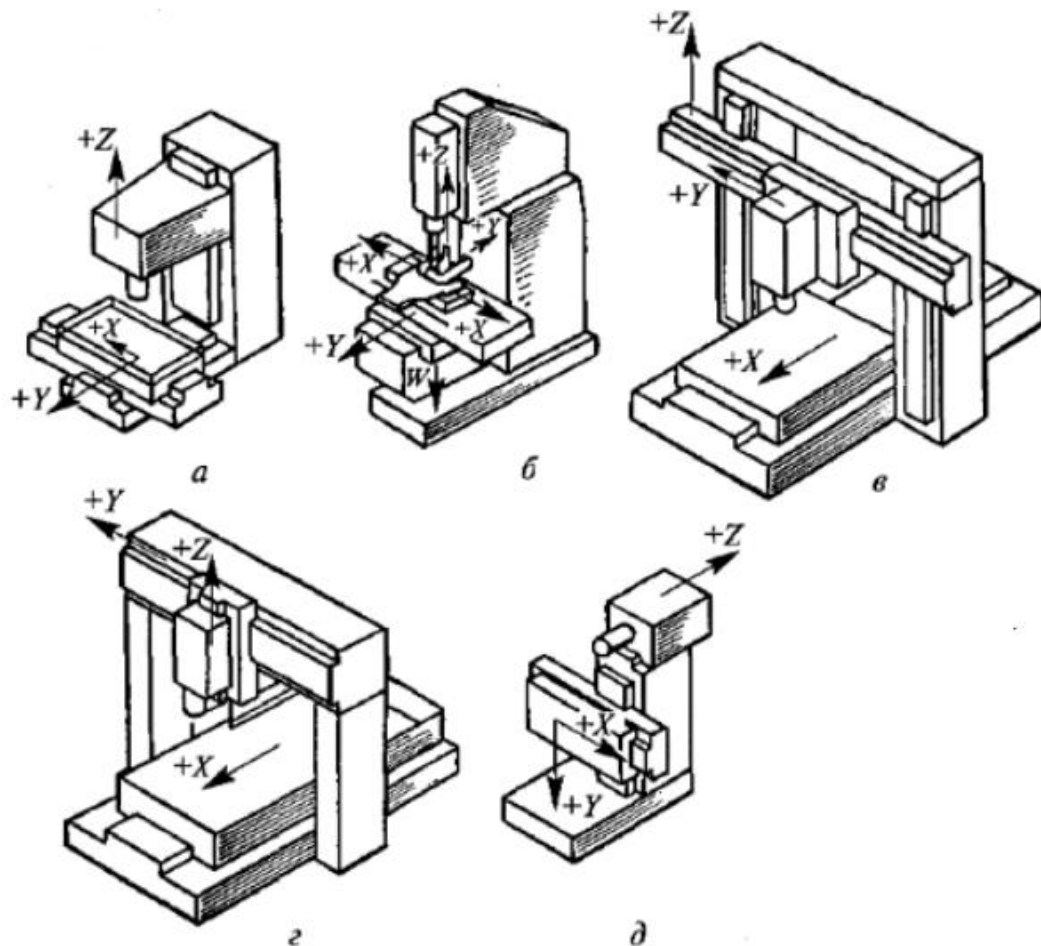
Компонування фрезерних верстатів з позначенням осей координат:
